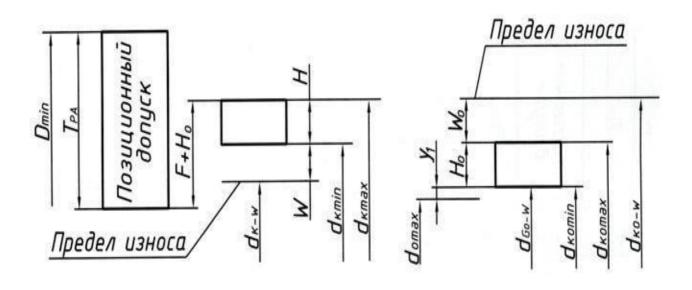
Схема расположения полей допусков калибров для контроля отверстий при наличии базового цилиндра
